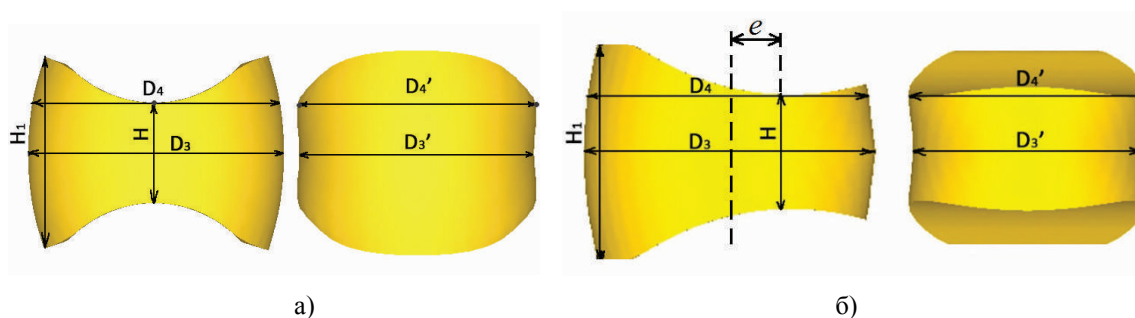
Схема обмера заготовки после осадки выпуклыми бойками: а – без эксцентриситета $e = 0$; б – с эксцентриситетом $e = 0,25$
